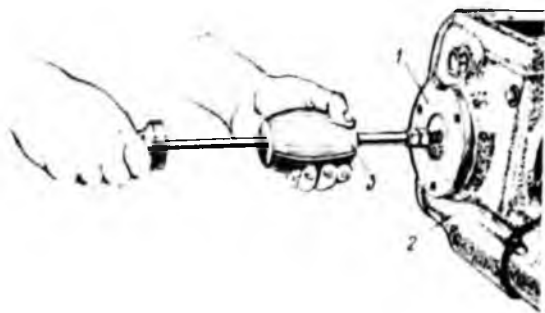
Извлечение цапфы люльки из корпуса насоса:
